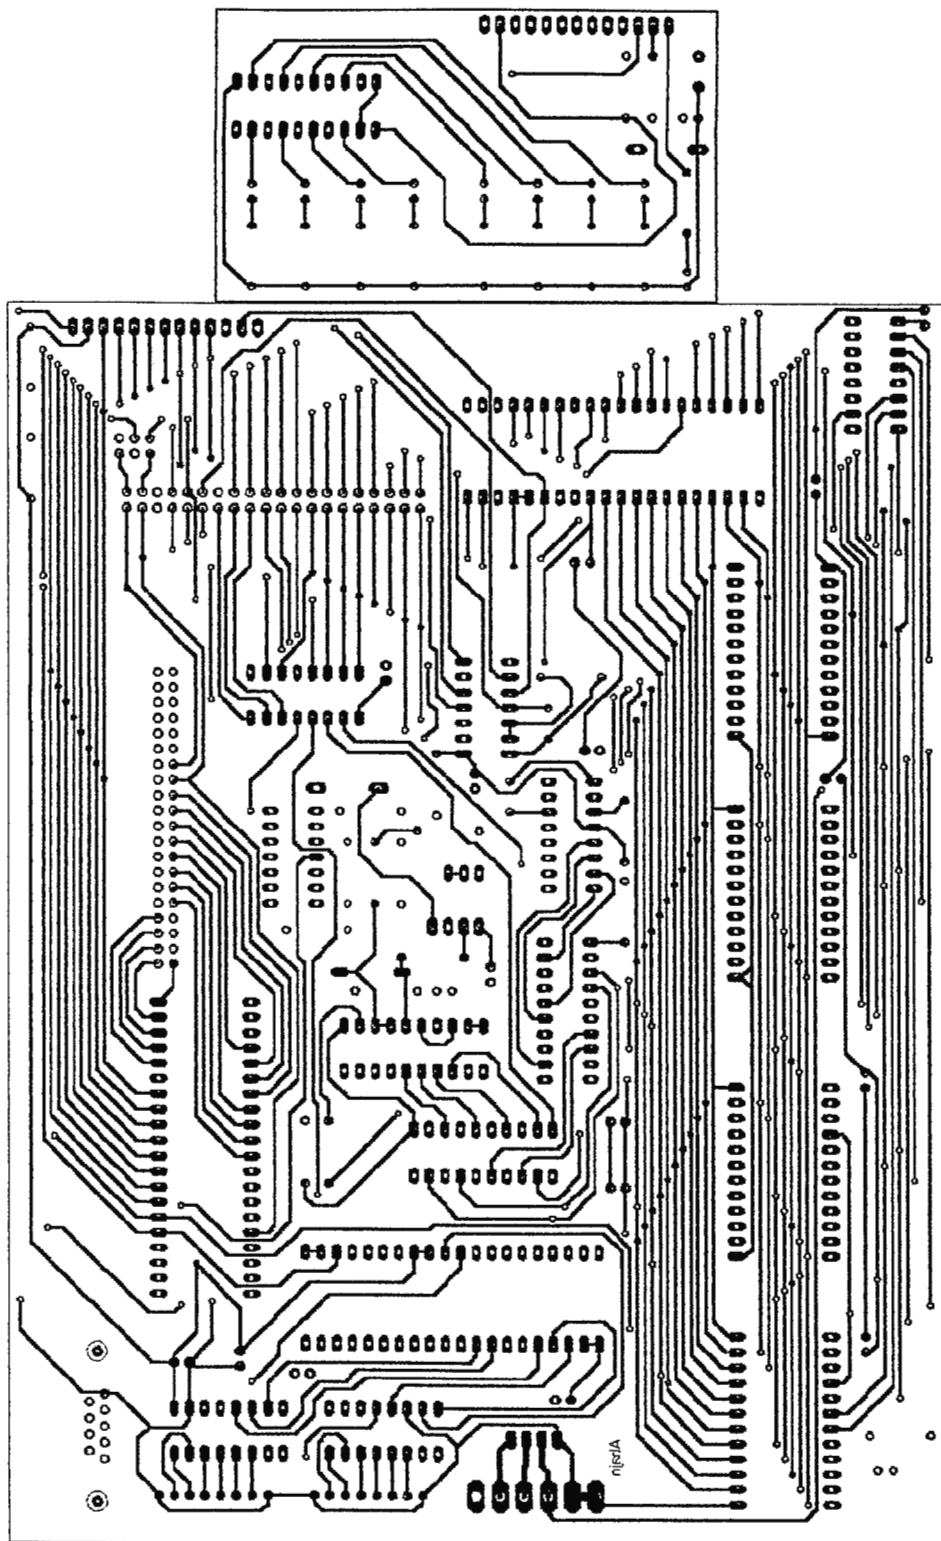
Circuito impreso del Módulo. Cara 2: Soldaduras.
